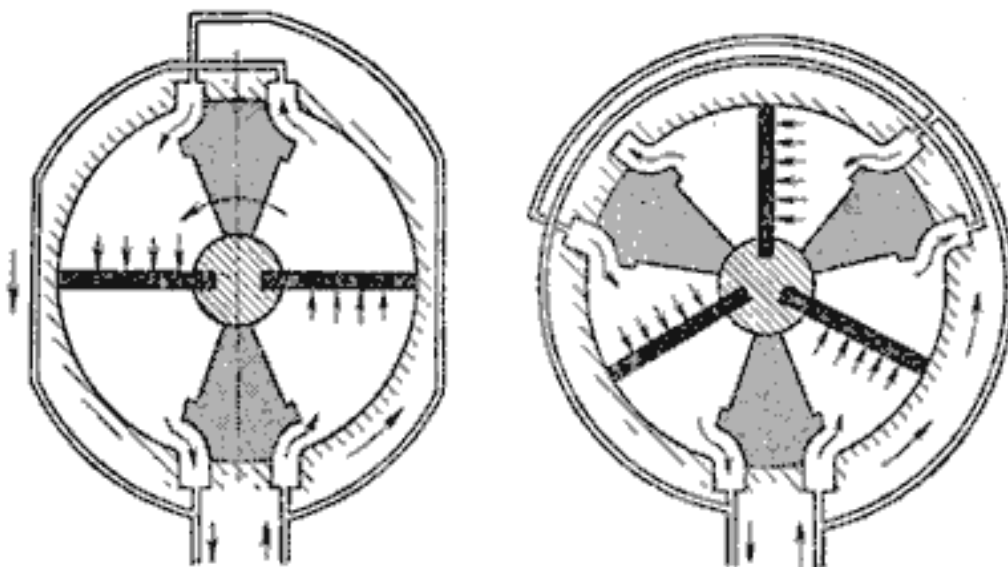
Поворотні гідроциліндри: а - дволопатевий; б – трилопатевий
